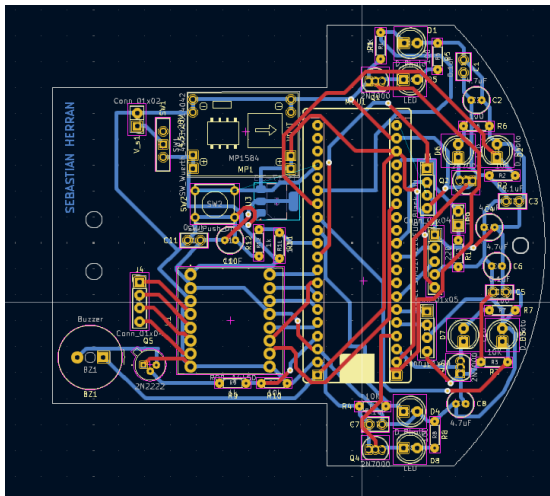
Diseño de la ubicación capas pistas etc de la PCB
